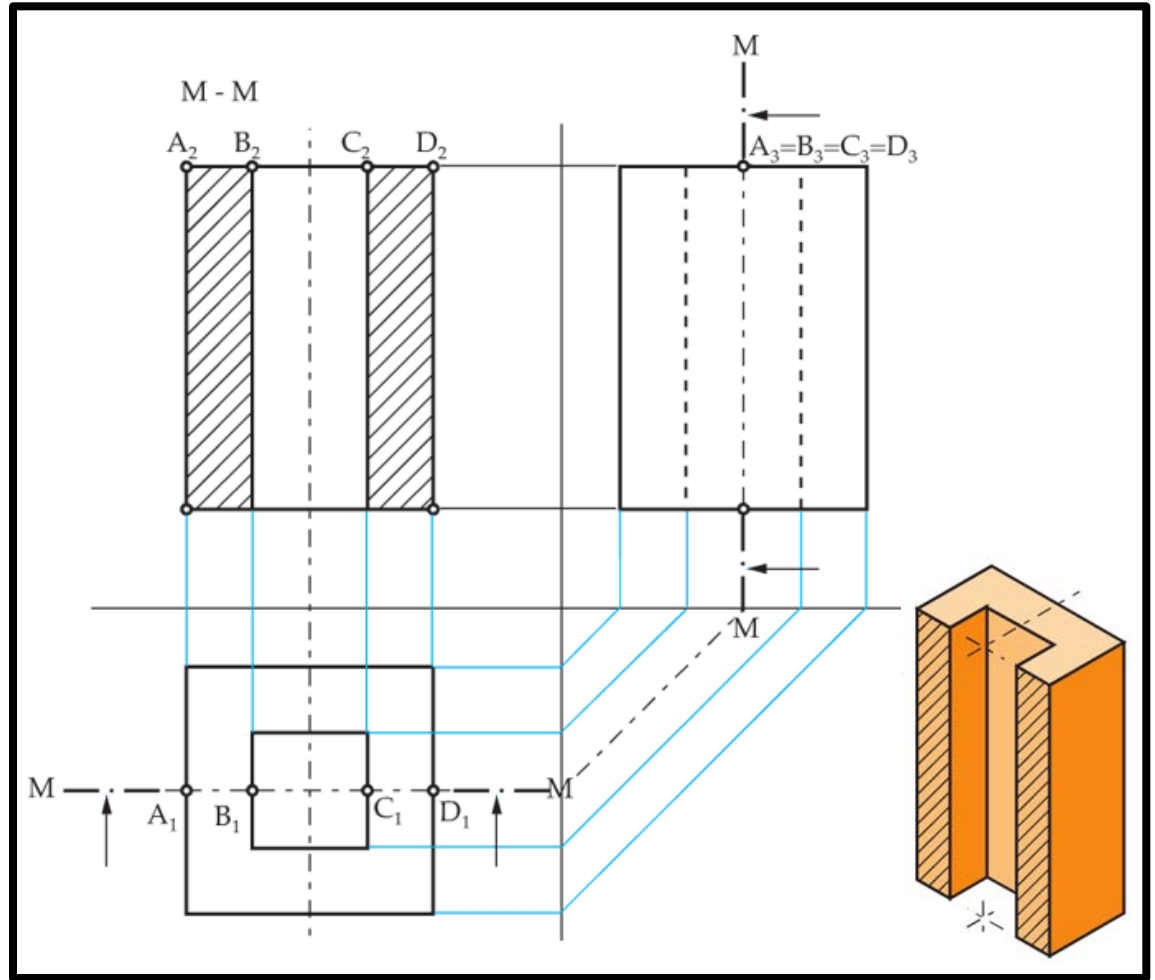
Sezione di un prisma cavo avente l'asse perpendicolare al p.o., mediante un piano M-M perpendicolare al p.o.
